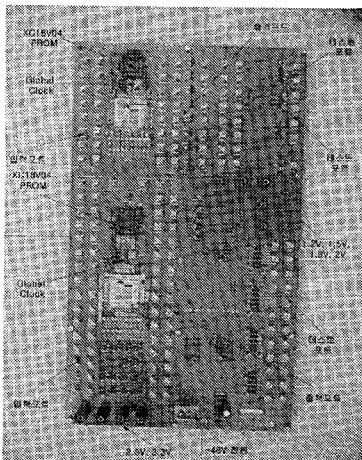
데이터 전달특성 분석을 위해 설계된 PCB
